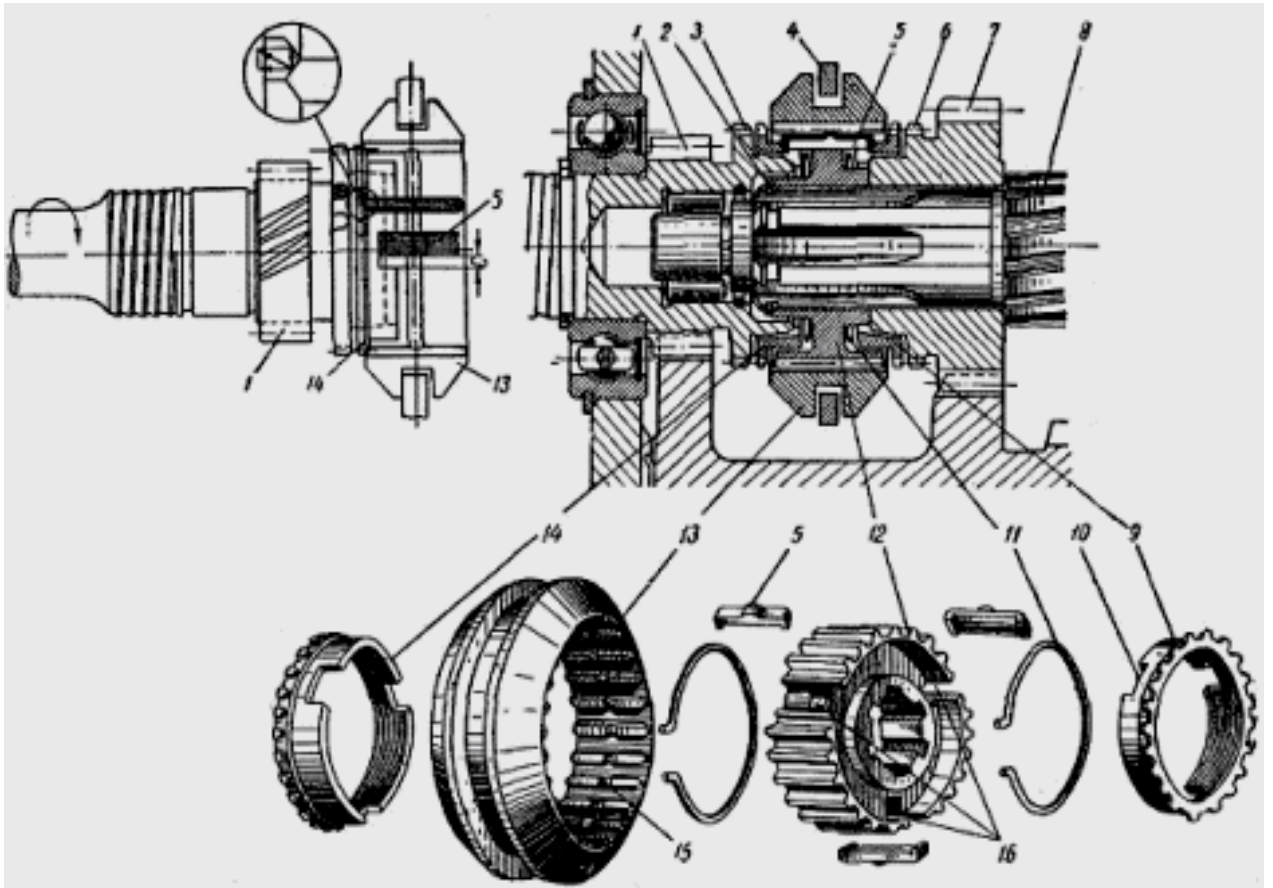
Синхронизатор коробки передач автомобиля "Москвич-407": 1 - шестерня первичного вала; 2 - стопорное кольцо; 3 и 6 - зубчатые венцы; 4 - вилка переключающего механизма; 5 - сухари; 7 - шестерня третьей передачи; 8 - илицы вторичного вала; 9 и 14 - бронзовые блокирующие кольца; 10 - пазы колец; 11 - два пружинных кольца; 12 - ступи
